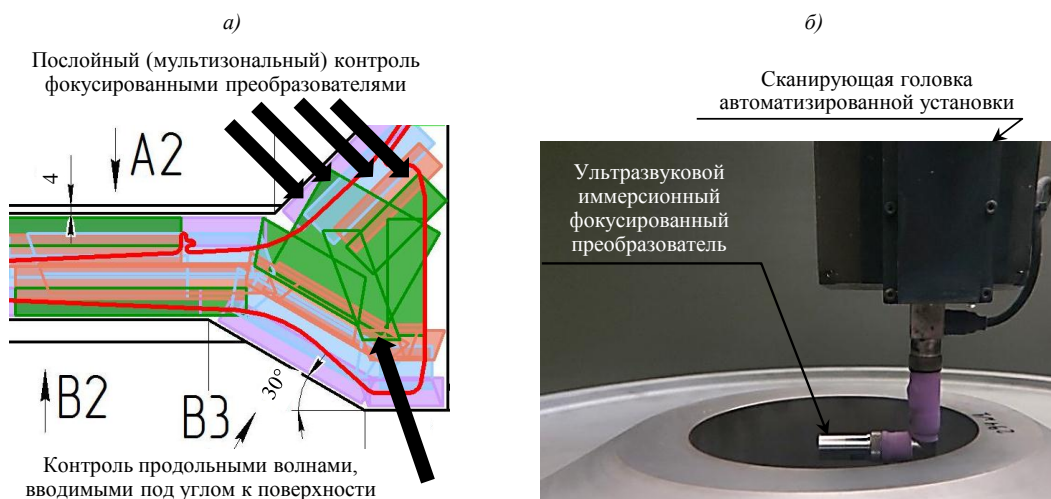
Автоматизированный иммерсионный ультразвуковой контроль заготовок дисков ГТД: *а* – фрагмент схемы прозвучивания заготовки диска в сечении (красная линия – чистовой контур детали); *б* – ввод ультразвуковых колебаний со стороны центрального отверстия заготовки диска
